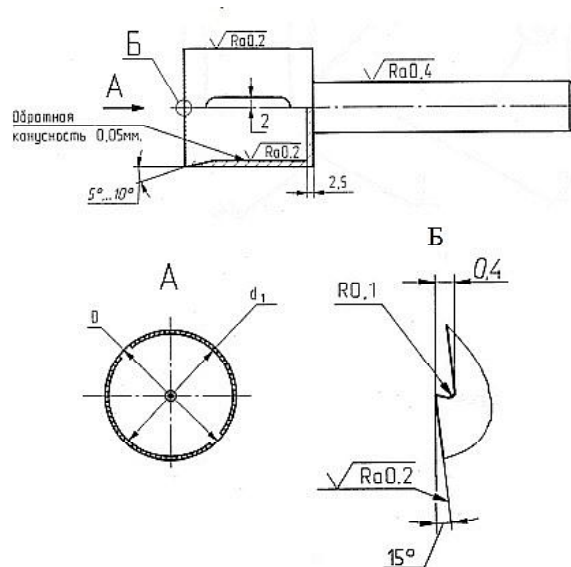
Чашечный зенкер для обработки отверстий среднего и большого диаметра
